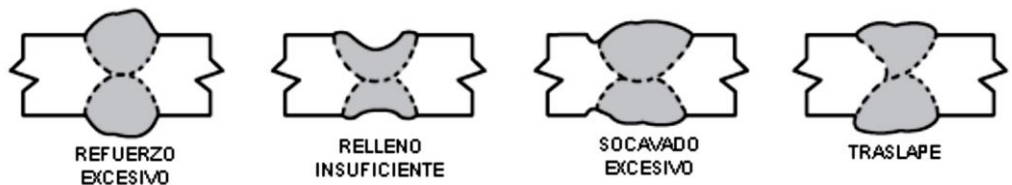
Perfiles no aceptables de soldadura de ranura [4].
